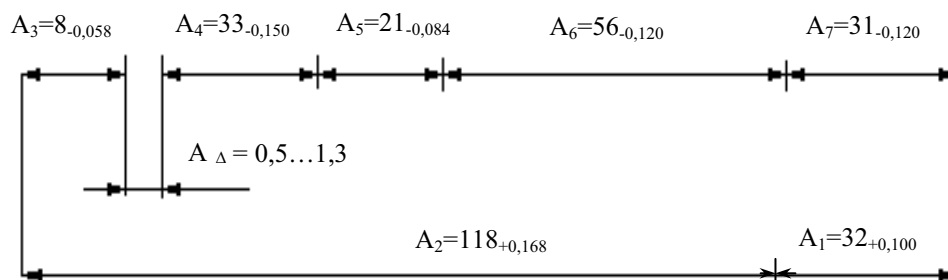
Схема размерной цепи с номинальными размерами и допусками
